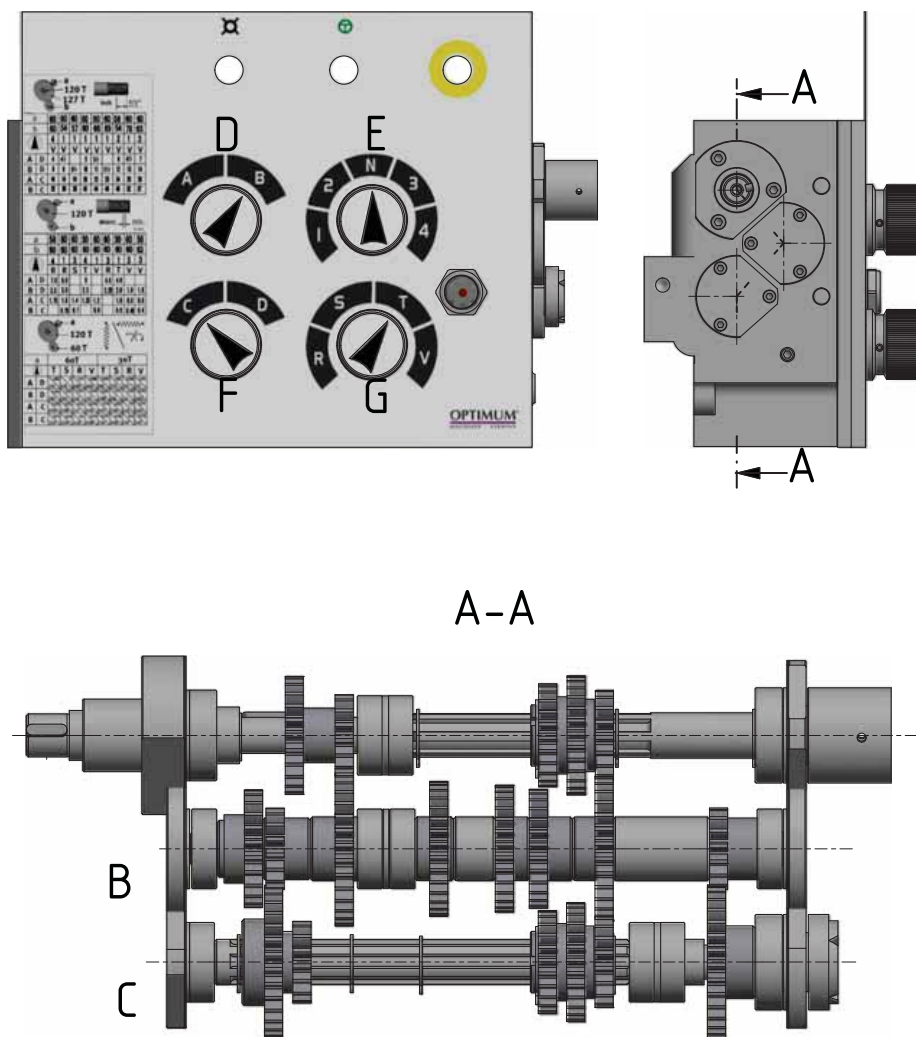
Vorschubgetriebe 2-6 - Feed gear 2-6
